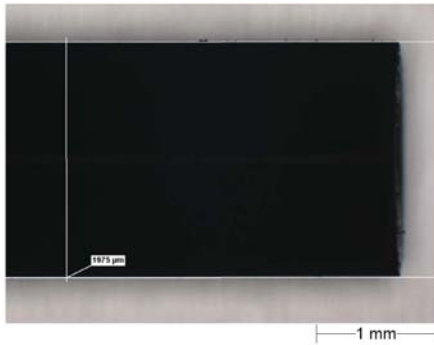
Vermessung des Durchmessers einer Flachbodenbohrung am Silikonkautschukabdruck
